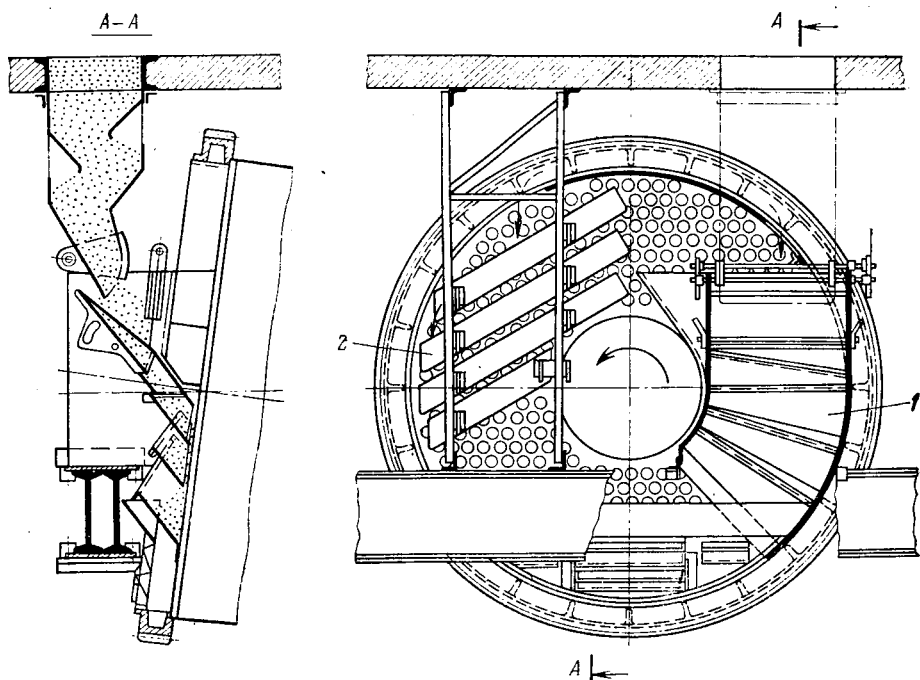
Загрузочное устройство паровой трубчатой сушилки
